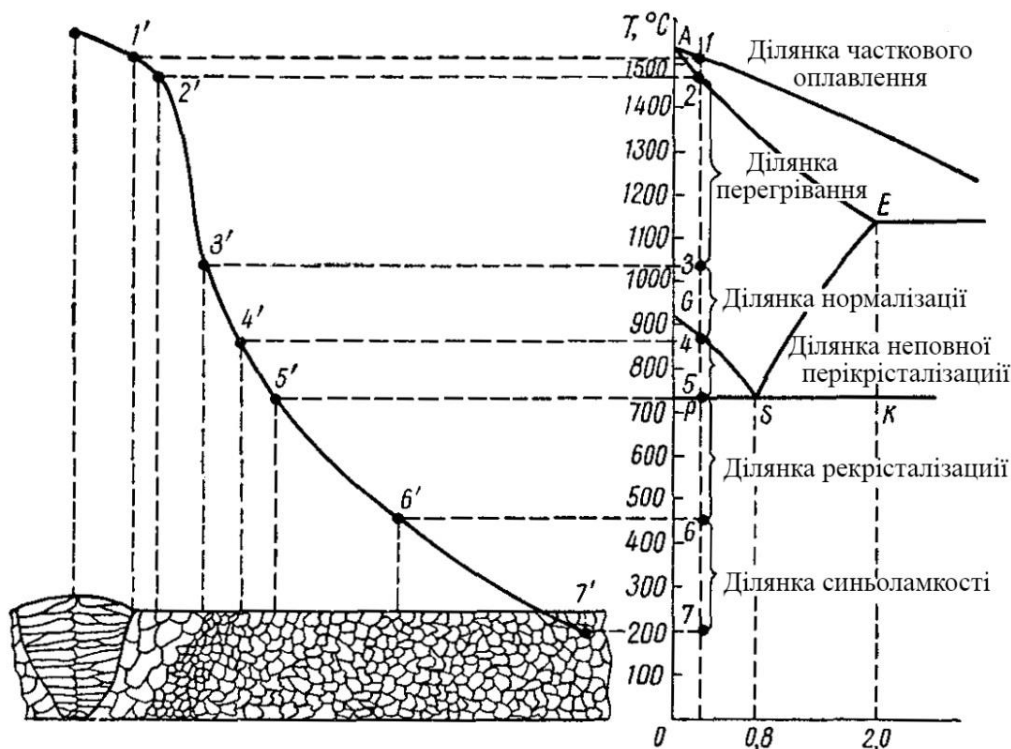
Схема будови однопрохідного зварного з'єднання вуглецевої сталі
